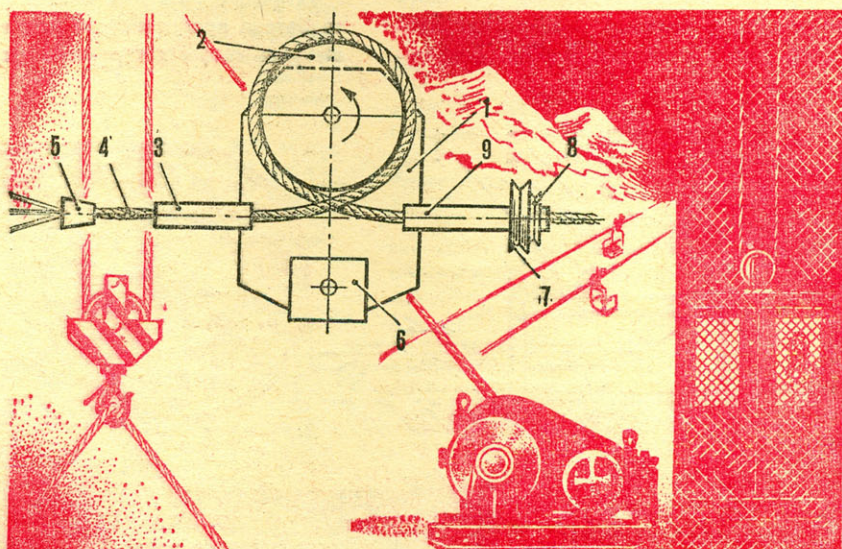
Деформатор, «исправляющий» канаты: 1 — основание; 2 — шкив для перекручивания каната; 3, 9 — полые опоры; 4 — канат; 5 — калибрующие пластины канатовыводящей машины; 6 — противовес; 7 — шкив клиноременной передачи; 8 — фрикцион.
